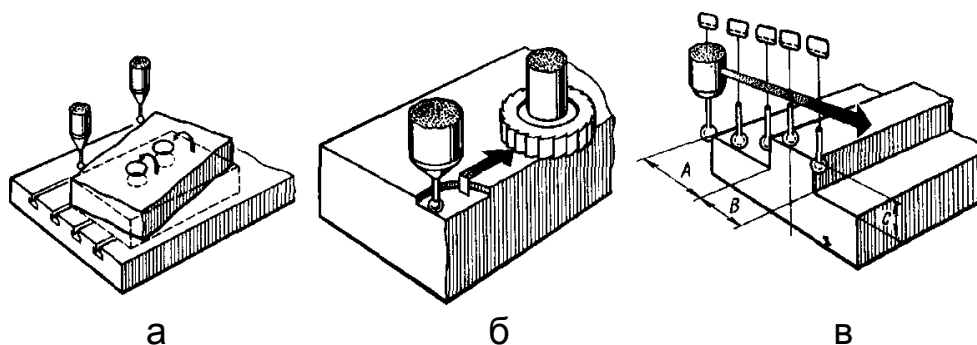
Схеми застосування ВГ для вимірювання: а – похибки установлення заготовки; б – величини припуску; в – розмірів деталі
